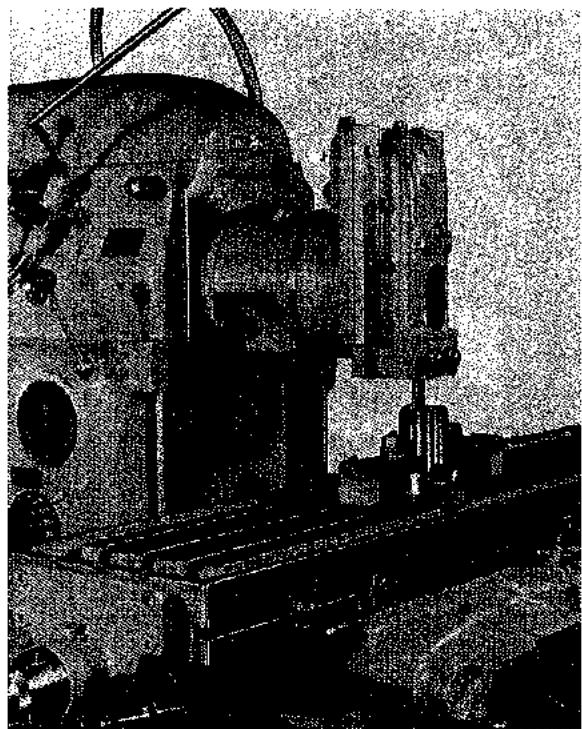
Ranurado de un casquillo empleando el cabezal de ranurar (Cincinnati Milling Machine Co.)
